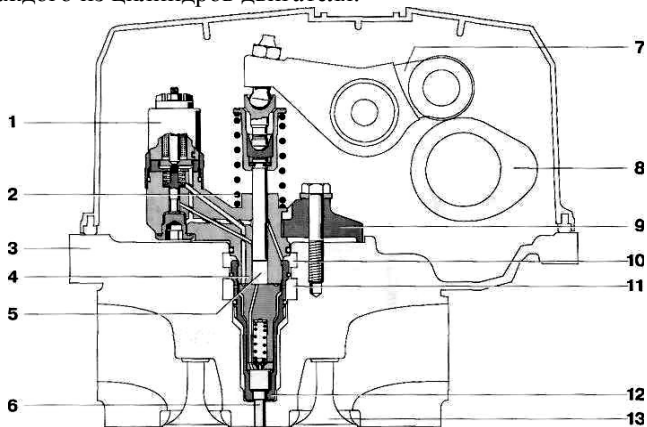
Установка насос-форсунки в головке блока цилиндров двигателя:
